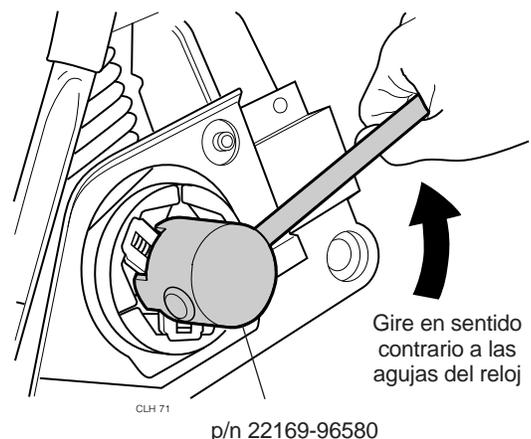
Ajuste de Maza del embrague en el cigüeñal
